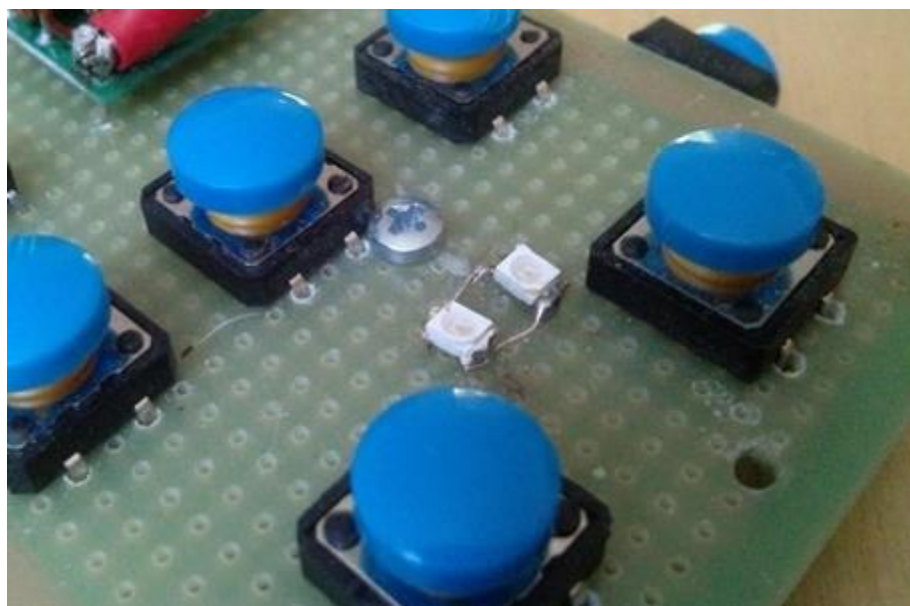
Schemat połączenia przycisków – strona lewa
